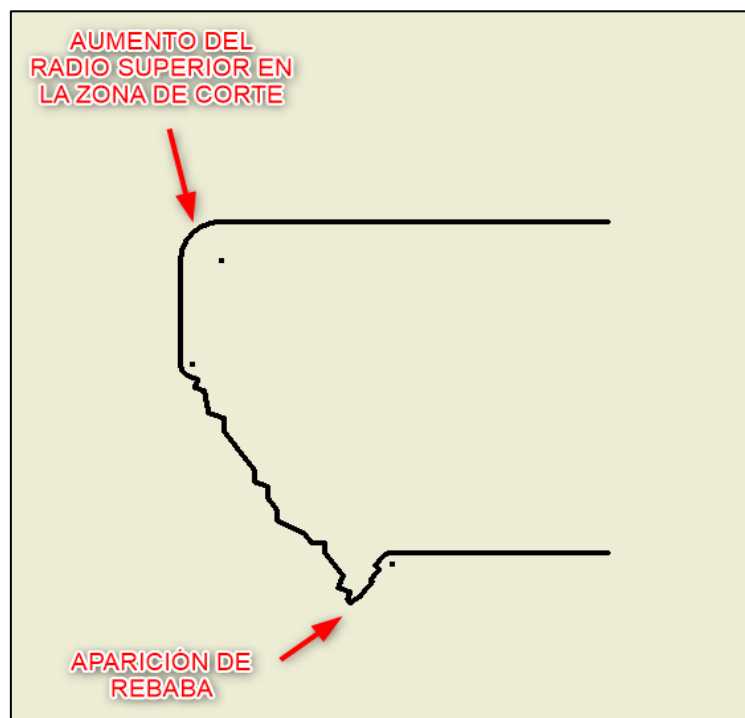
Esquema de corte realizado con un juego de tolerancias excesivamente grande.
